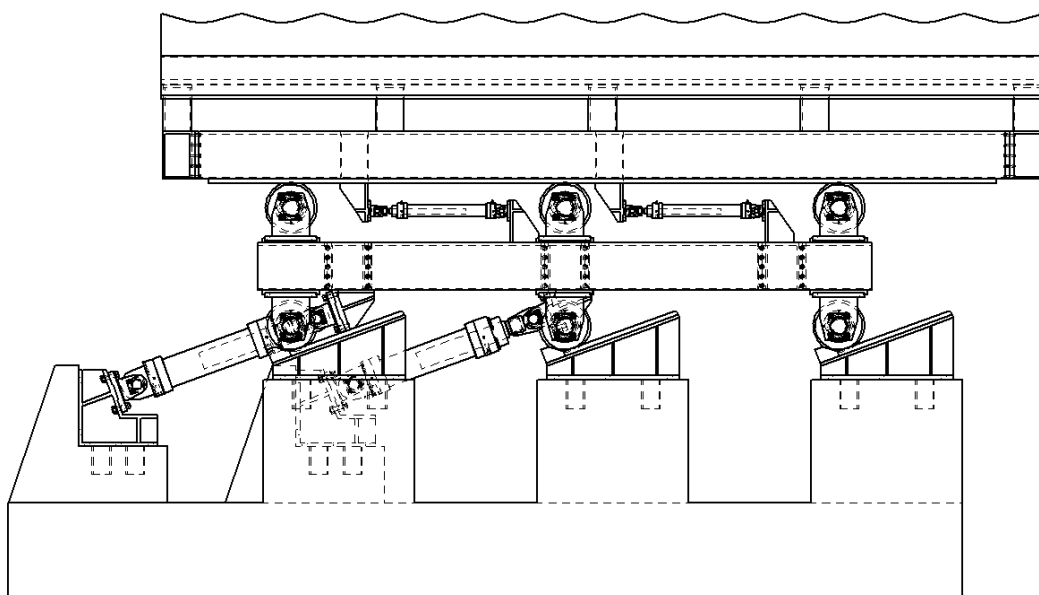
Částečný řez zobrazený přímočarý motor pro horizontální pohyb.
